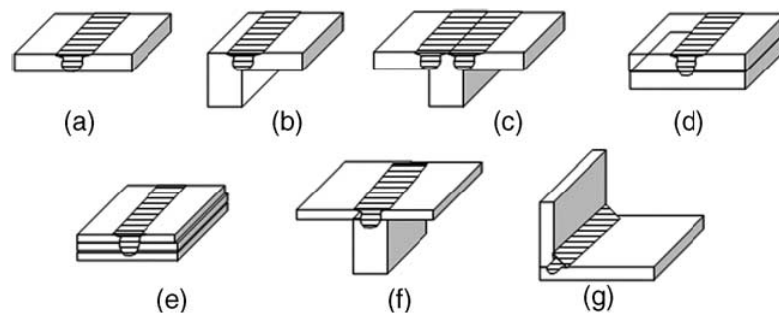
Configurações de junta passíveis de serem soldadas pelo processo de SFL
